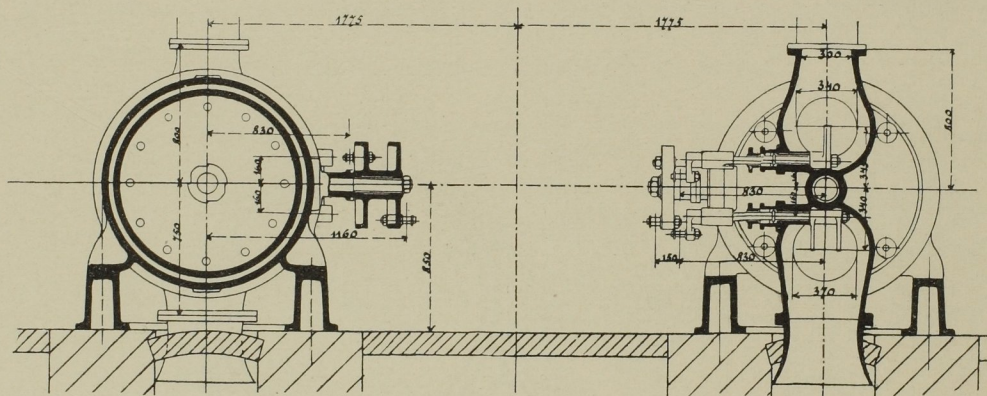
Ansicht und Querschnitt des Windcylinders. Masst. 1:40.
